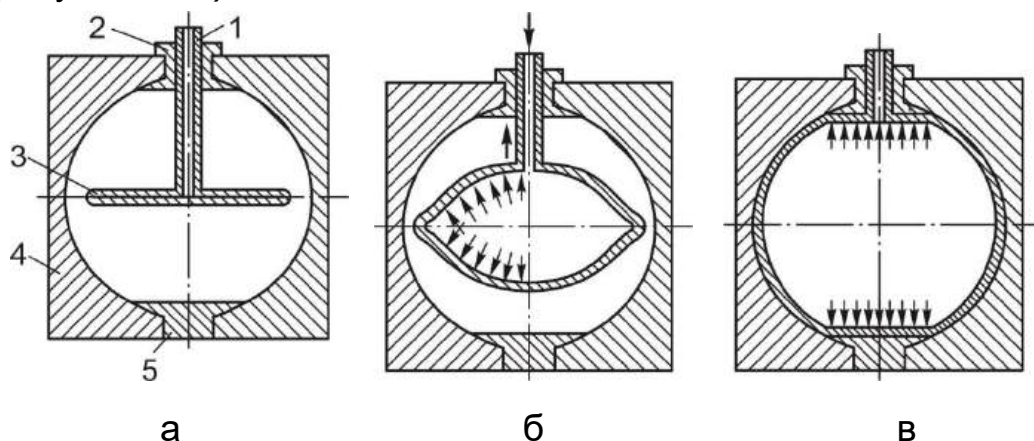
Схема виготовлення шарових балонів: а – установка заготовки в оснащення; б – формування заготовки; в – дифузійне приварювання штуцера і фланця; 1 – труба подачі газу; 2 – штуцер; 3 – дискова заготовка; 4 – оснащення; 5 – фланець
